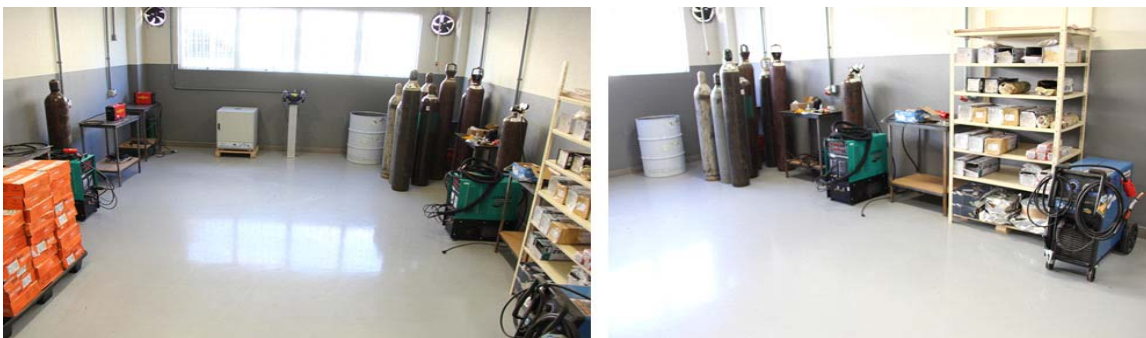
Equipamentos para soldagem (fontes, equipamentos de solda eletrodo, TIG, MIG, oxicorte).
